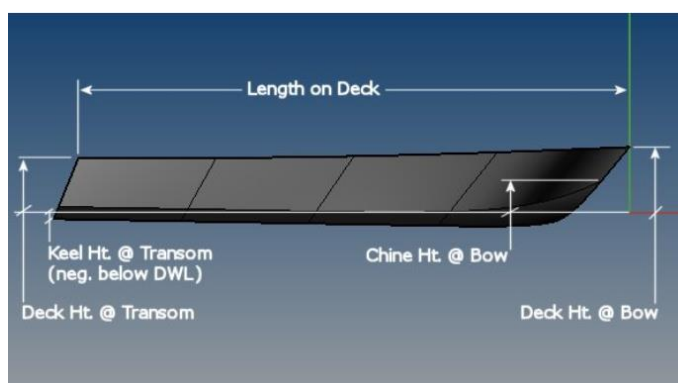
Dimensiones perfil – Fuente: Quick Start Guide Orca 3d
